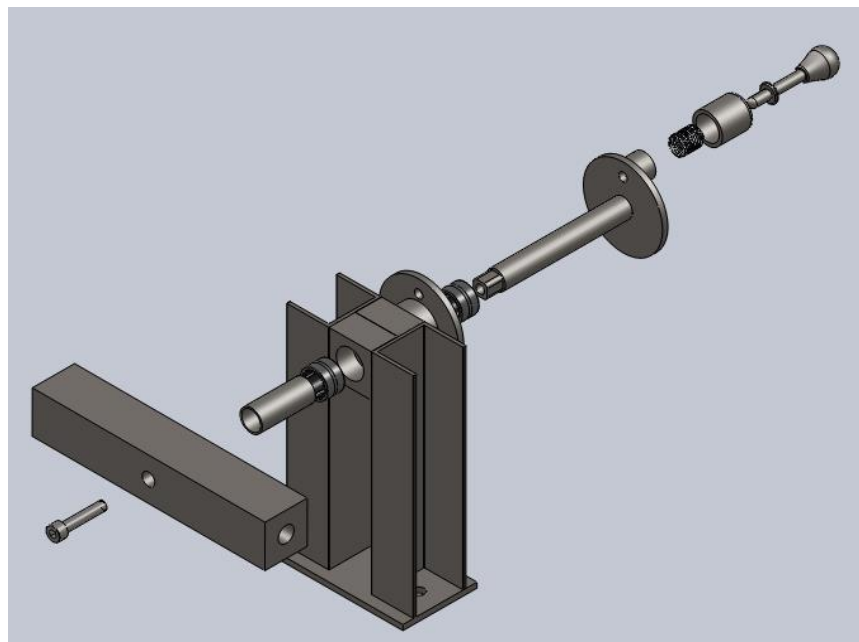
16. Explosionado soporte trasero potro de soldadura
